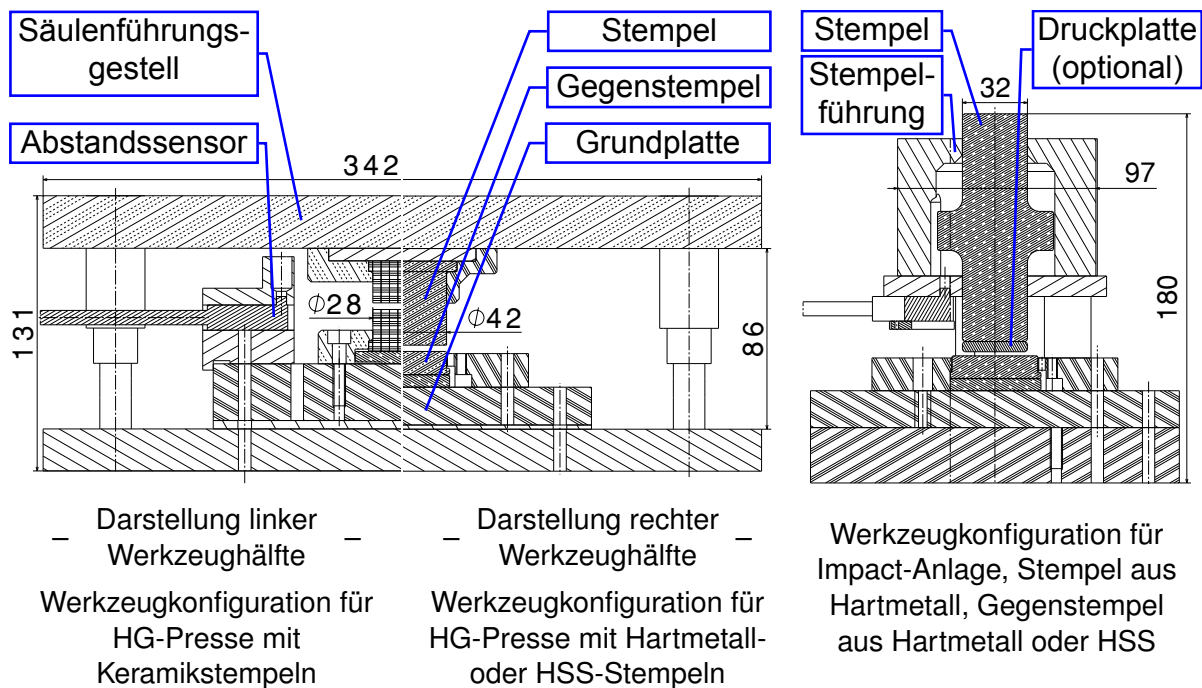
Modularer Werkzeugsatz für Stauchversuche (Bemaßung in mm)
